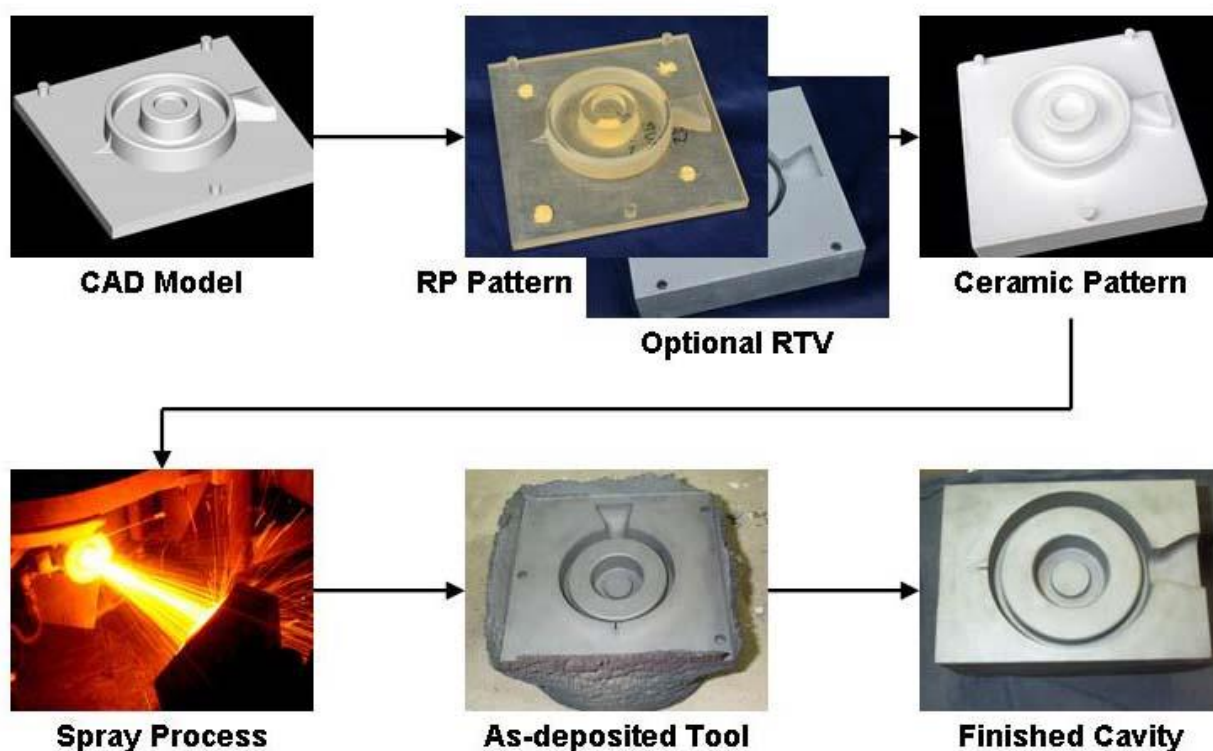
Процесс получения изделий напылением металла на керамическую модель
